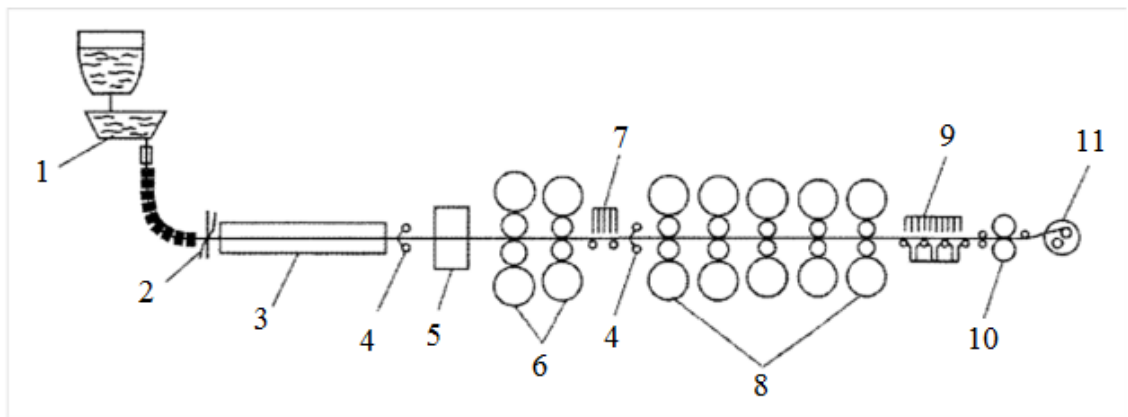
Схема агрегата DSP: 1 – машина для розливання сталі; 2 – маятникові ножиці; 3 – нагрівальна туннельна піч; 4 – механізми видалення окалини; 5 – кліть с вертикальними валками для розрихлення окалини; 6 – чорнові прокатні кліти; 7 – устаткування для охолодження безперервно-литих зливків; 8 – безперервна чистова група клітей; 9 – холодильник; 10 – летучі ножиці; 11 – моталка
